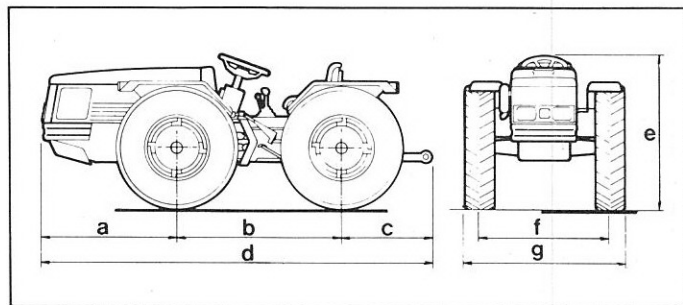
Dimensions hors tout du Supertigre-Tropical.
